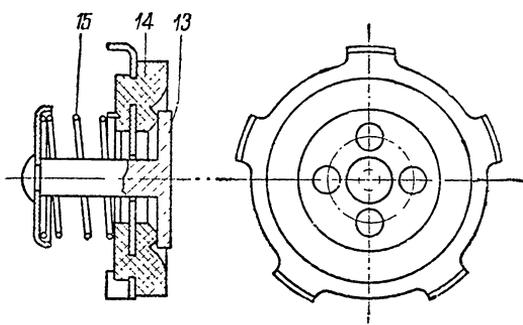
Клапан главного цилиндра в сборе (нумерация деталей та же, что на рис. 138)
